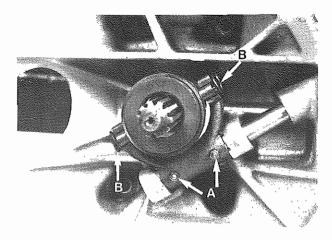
A - Spine di fissaggio Fixing pins B - Molle di ritegno Retaining springs
